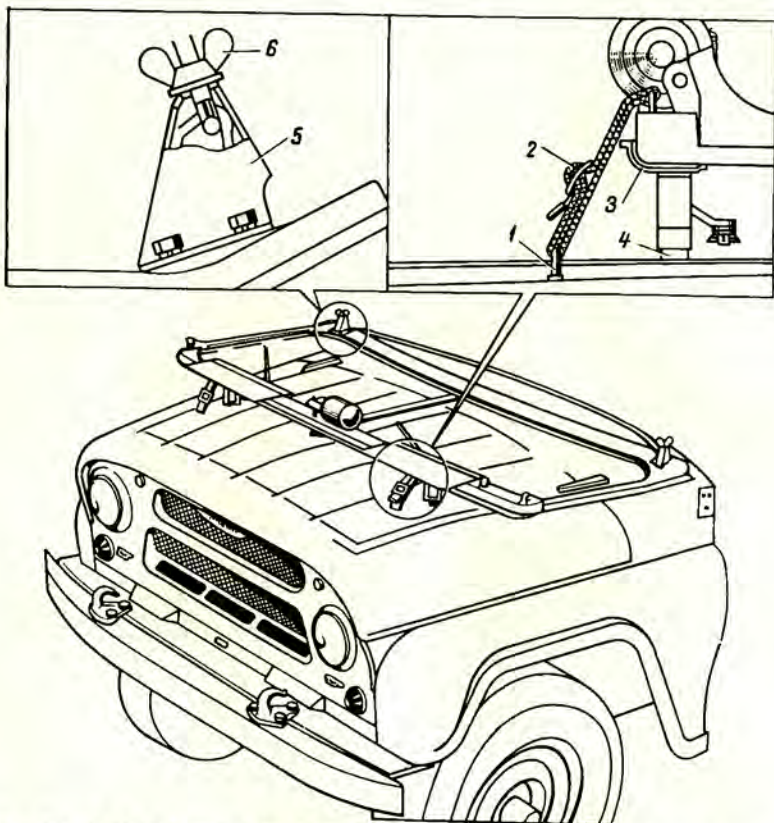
Befestigung des abgeklappten Windschutzscheibenrahmens:
